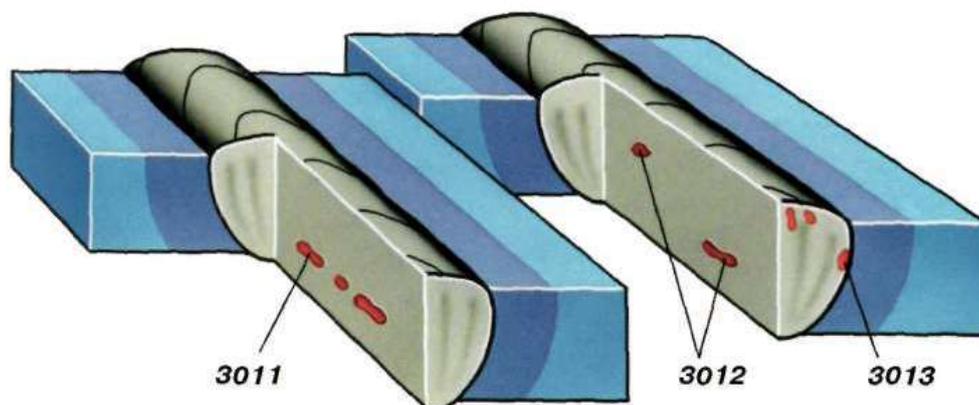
Дефект сварного шва по типу наличия шлаковых включений
